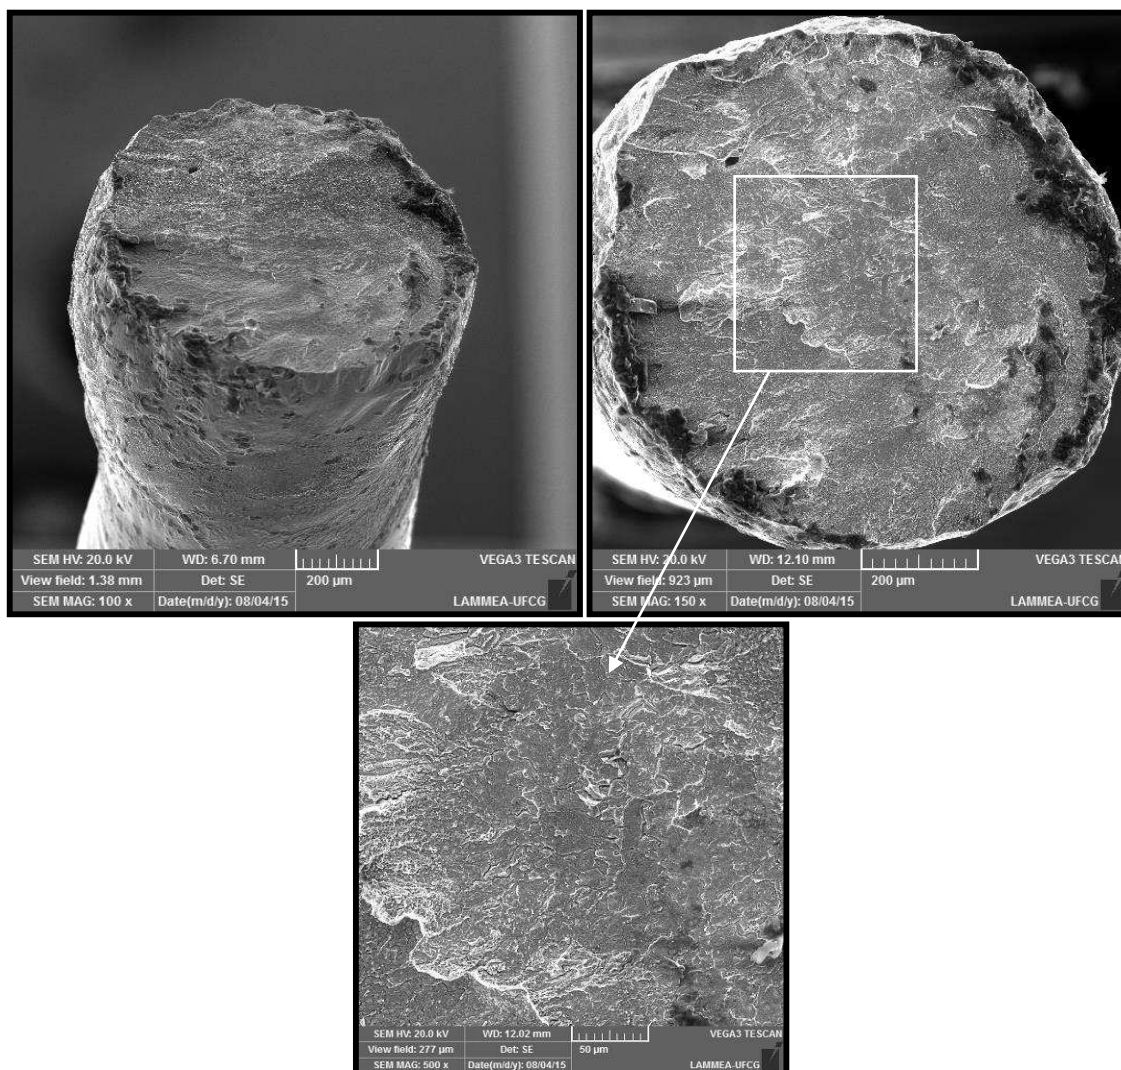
Superfície de fratura do fio atuador soldado na configuração 8ms/65% e testado a 40°C.
